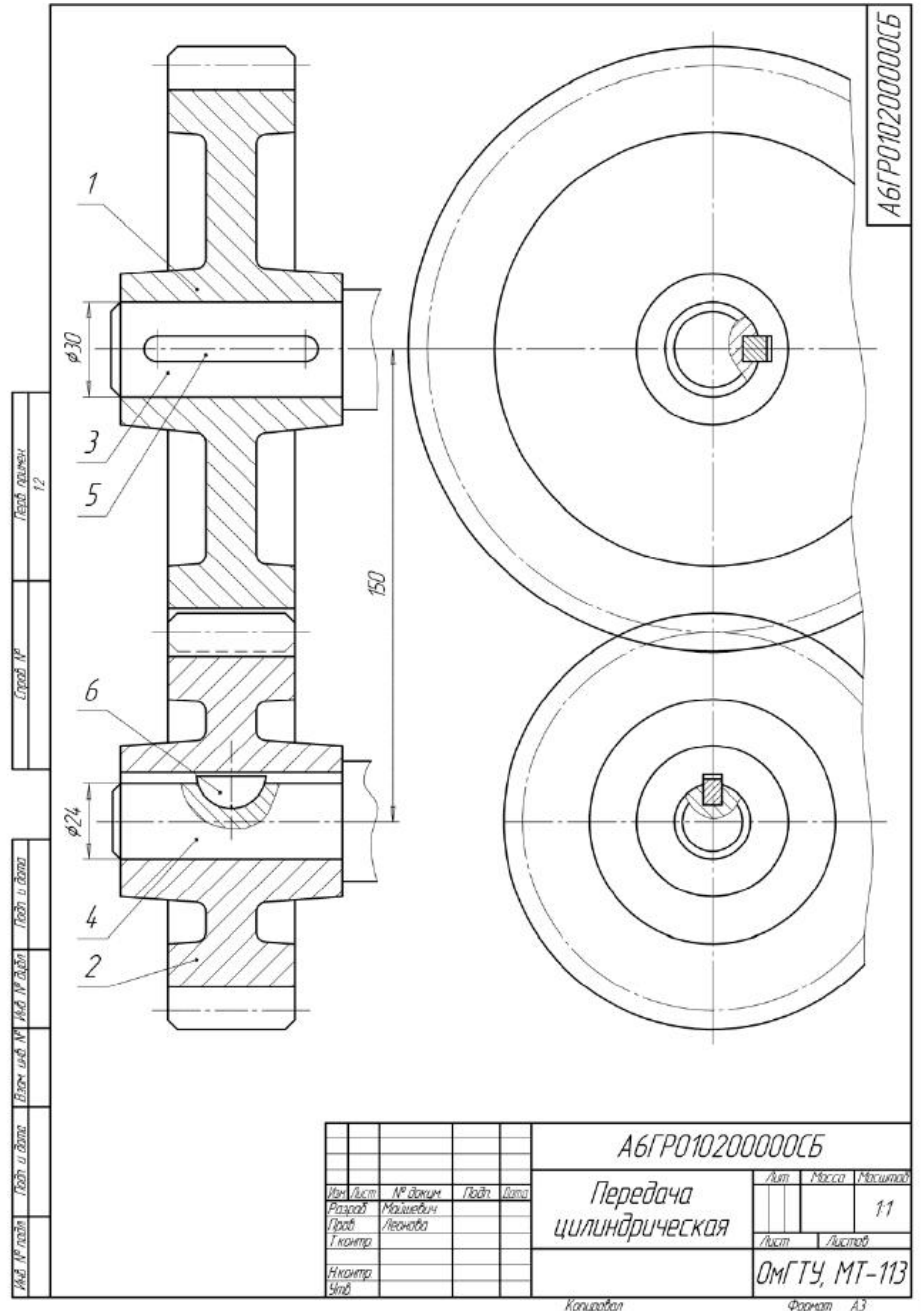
Сборочный чертеж зубчатой передачи со шпоночным соединением валов и колес
